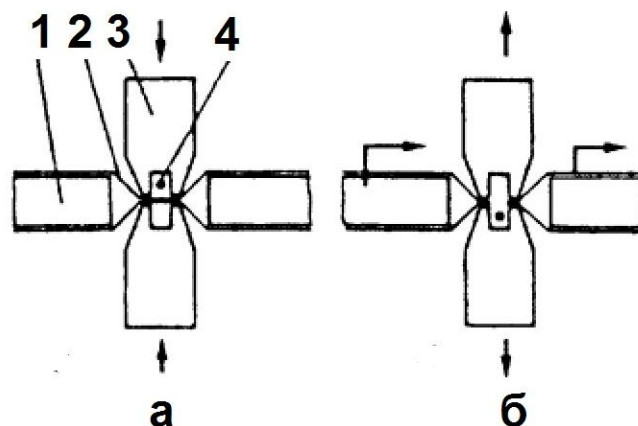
Двосторонній штамповий пристрій для поперечного зварювання і розрізання нагрітим дротом пакувального рукава
